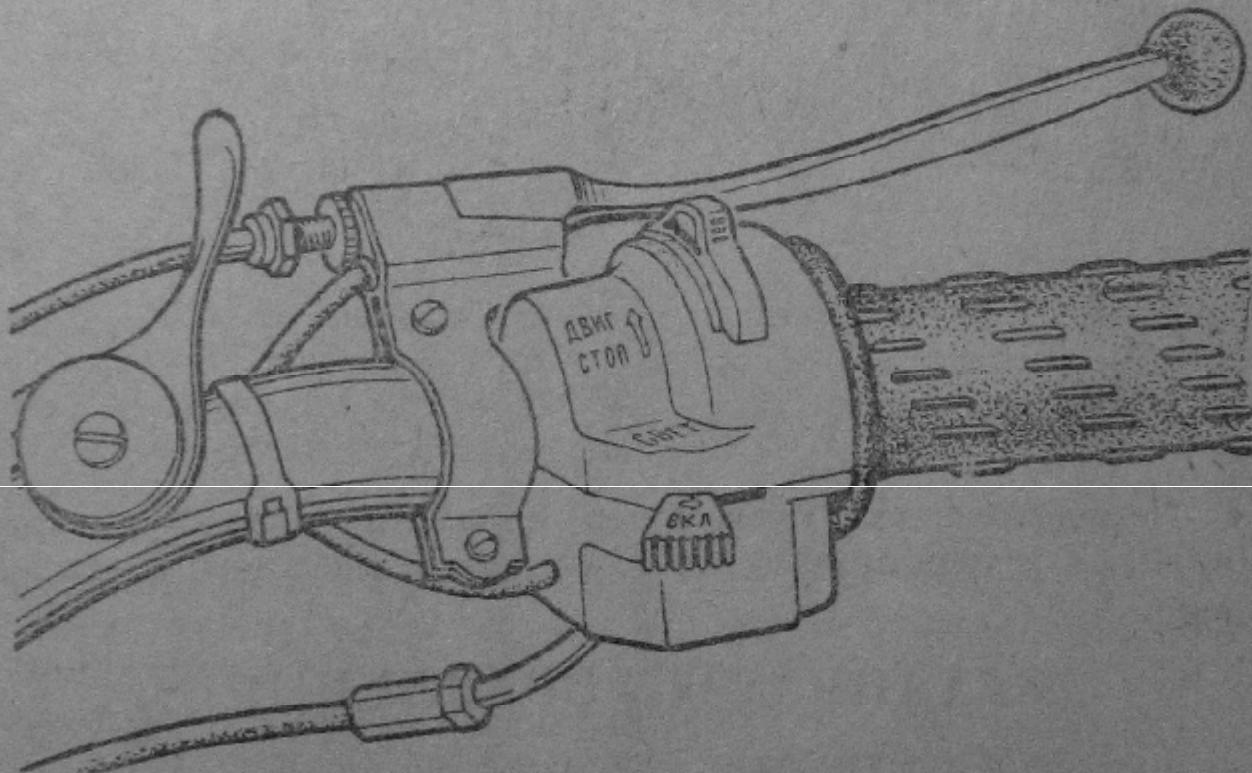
Включатель света, аварийный выключатель зажигания и рычаг топливного корректора
